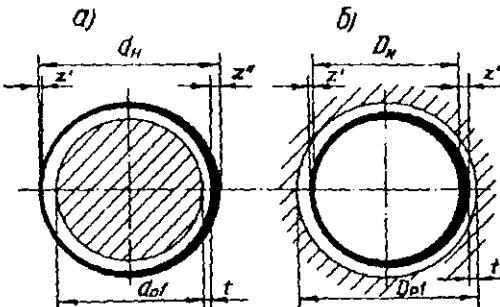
1. Схема определения ремонтных размеров: а) – для вала; б) – для отверстия.
